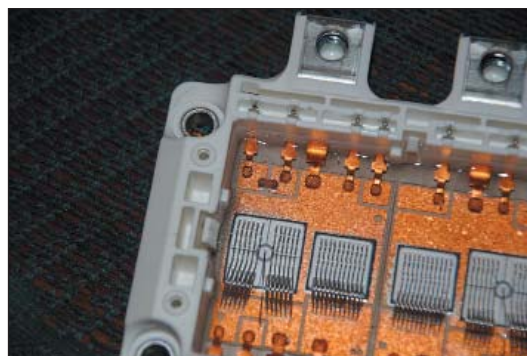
Размещение NTC-резистора на поверхность керамической DCB-подложки
